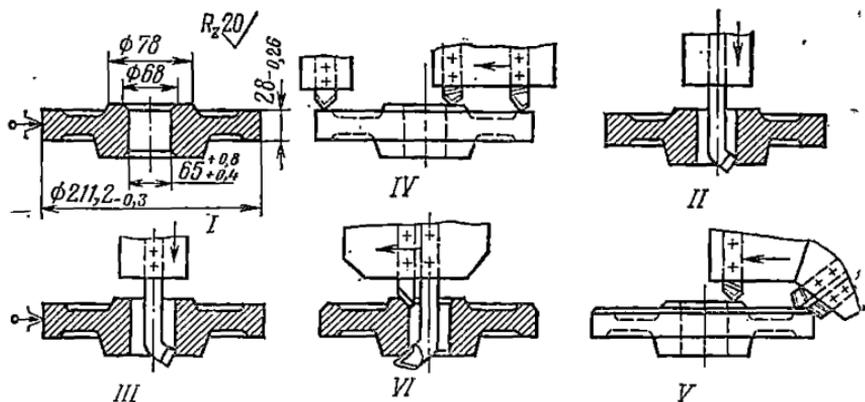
Наладка вертикального шестицилиндрового токарного полуавтомата для обработки заготовки зубчатого колеса с установкой и закреплением в патроне.
